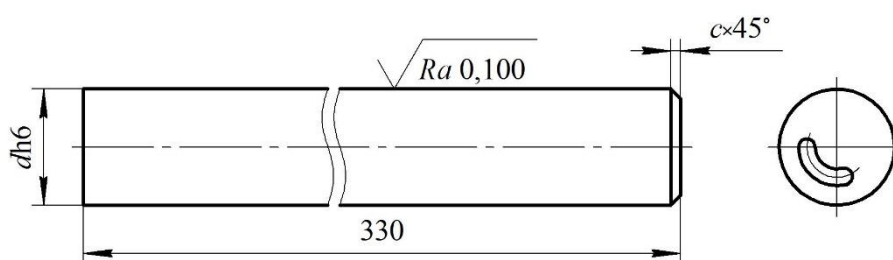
Твердосплавная заготовка ружейного сверла, получаемая методом мундштучного прессования
